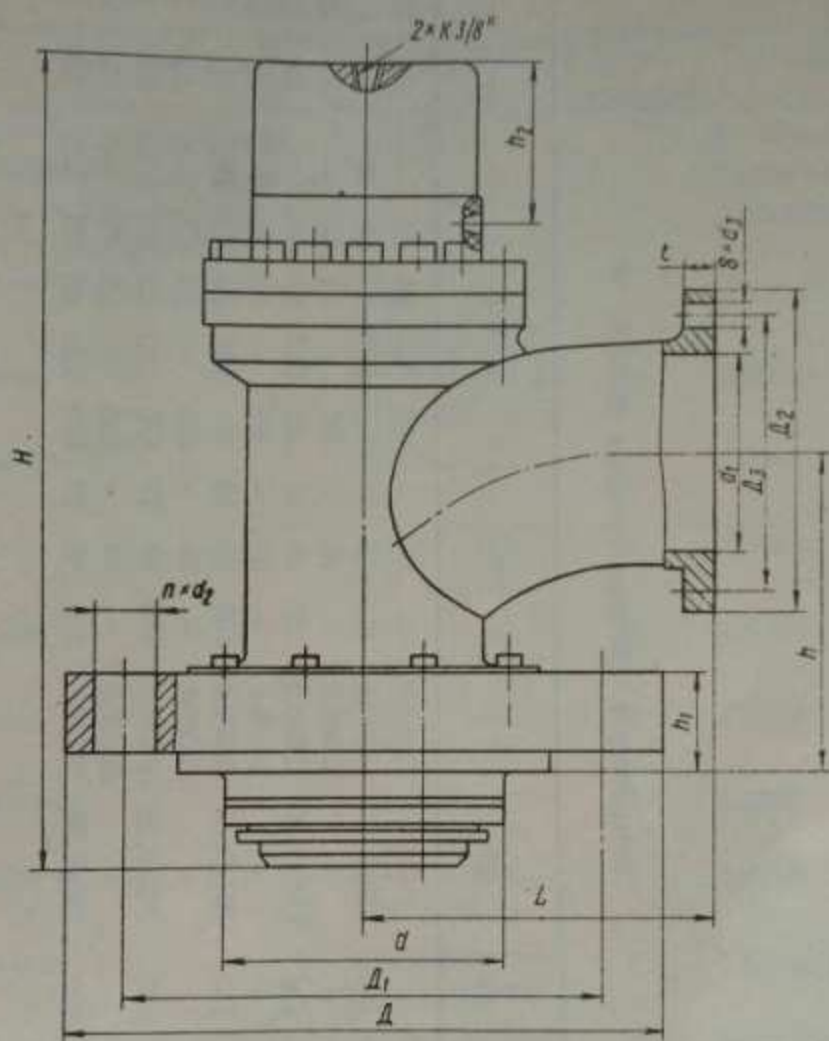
Габаритные и присоединительные размеры гидроцилиндров на-
